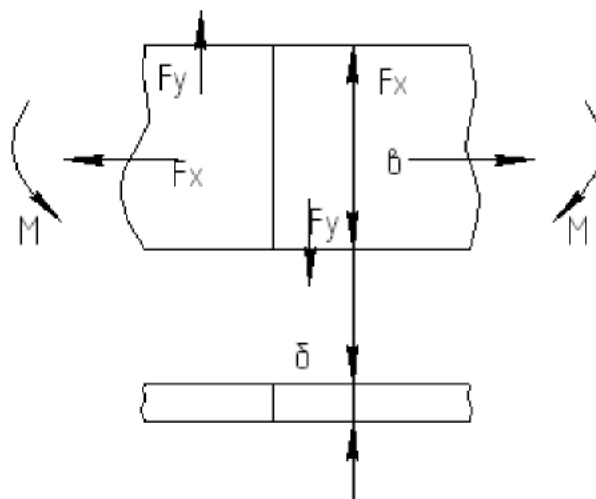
Нагрузки стыкового сварного шва
